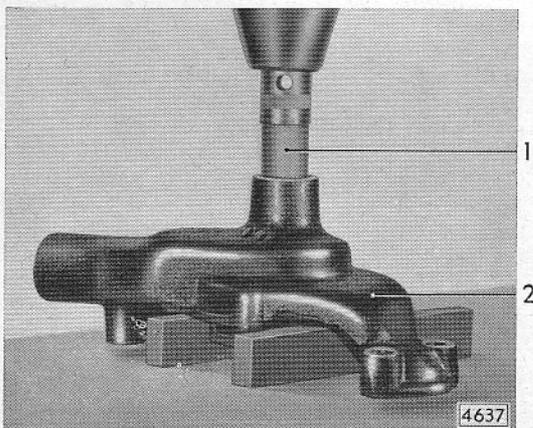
Auspressen des Zusammenbaues Welle mit Lager
